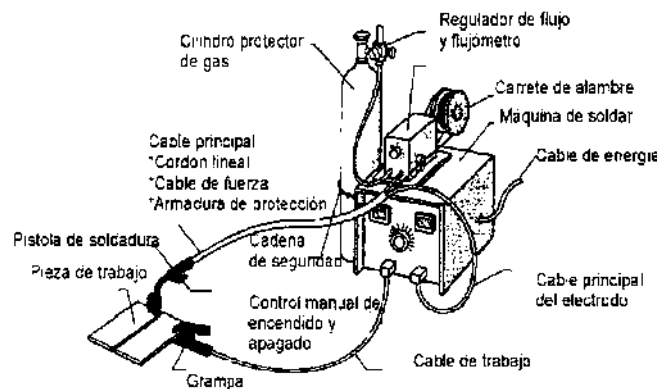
Proceso de soldadura MIG/MAG
